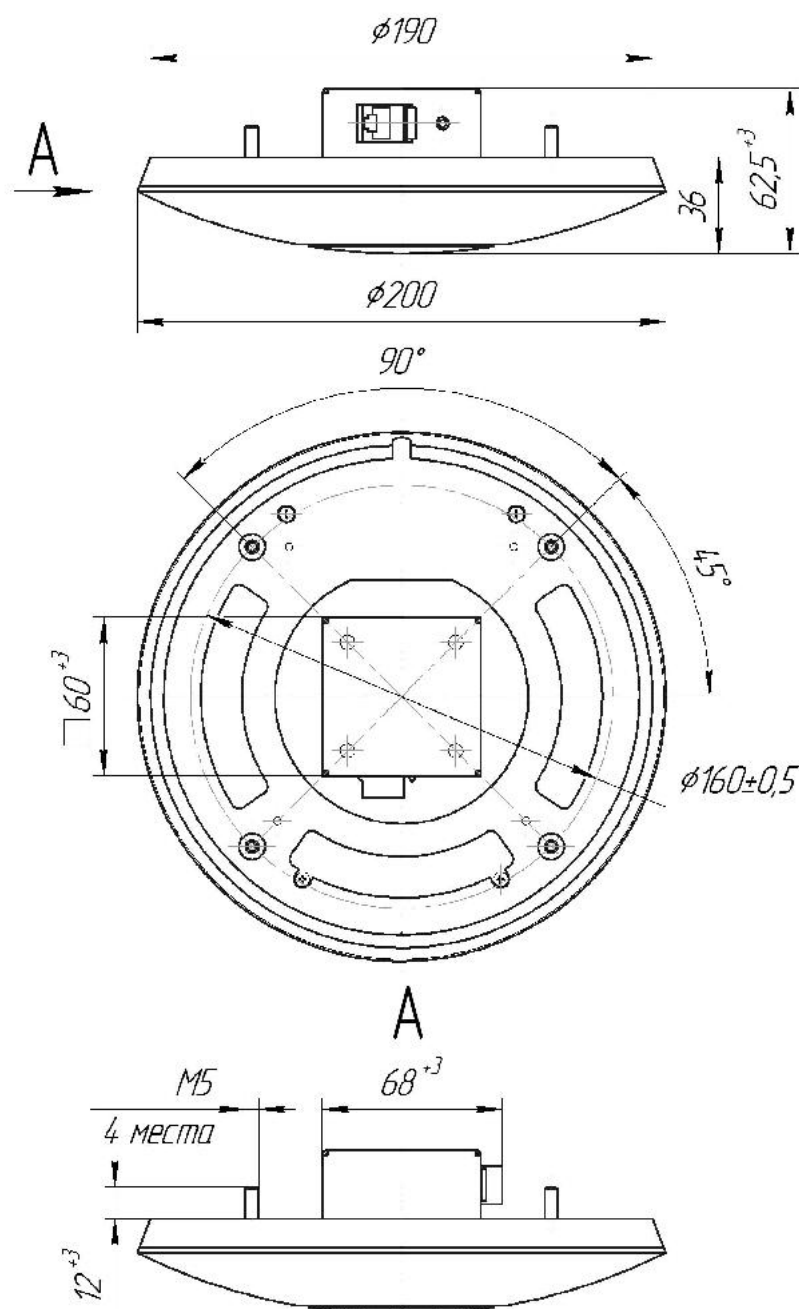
Габаритные и установочные размеры WIFI точки доступа
